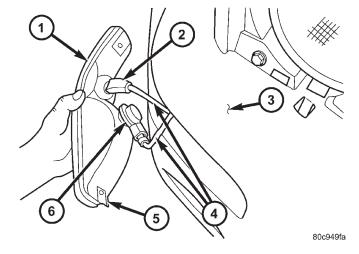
Desmontaje e instalación de bombilla de faro delantero
